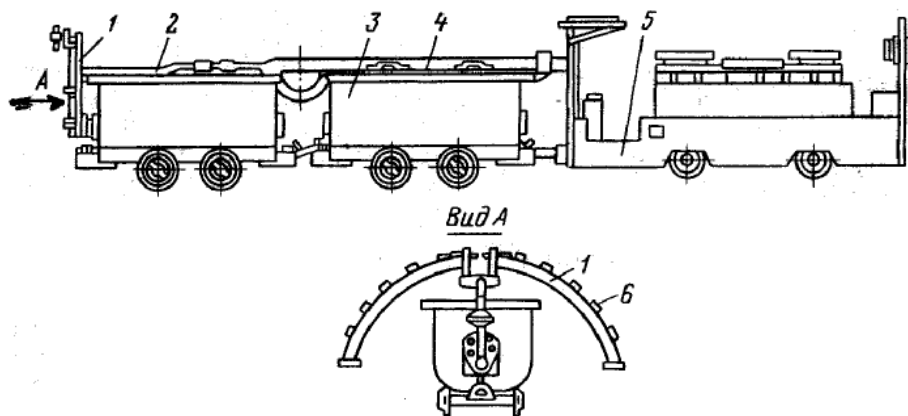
Агрегат білильний АП: 1 – робочий орган; 2 – напірний трубопровід; 3 – вагонетка; 4 – всмоктувальний механізм; 5 – акумуляторний електровоз; 6 – форсунки
